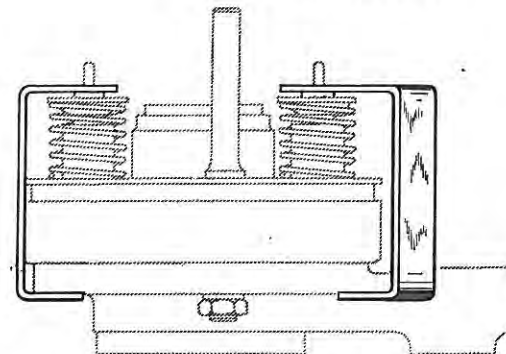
Haltevorrichtung für die Kolben der HD-Pumpe. Erhältl. unter 2284-T
